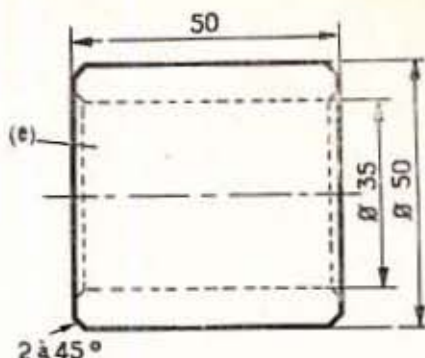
Cotes de la bague à réaliser pour montage sous presse
